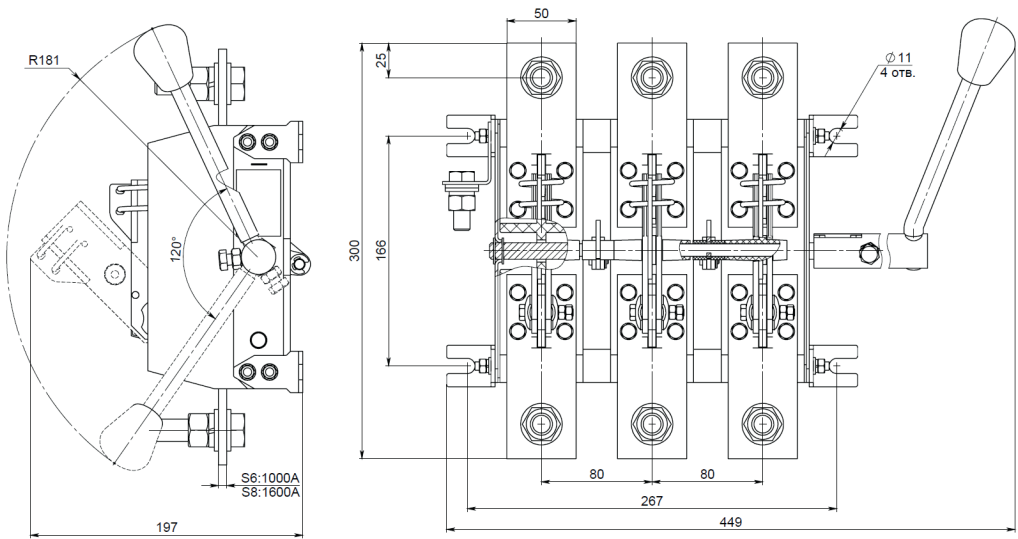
Разъединитель РЕ19-41(43)-32250-00 УХЛЗ с боковой смещенной рукояткой, заднего присоединения шин
